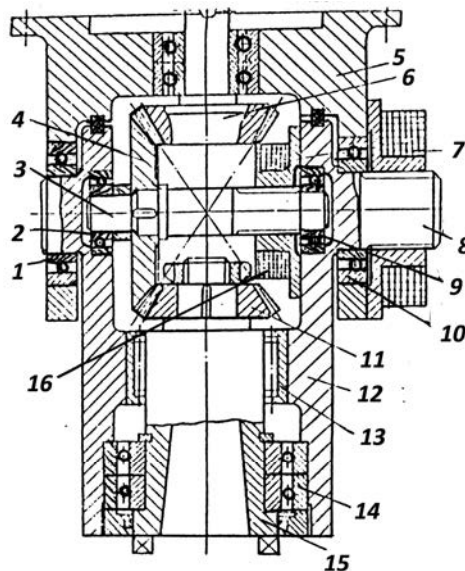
Передаточний механізм для перетворення обертального руху привода в круговий рух подачі або установочних переміщень
